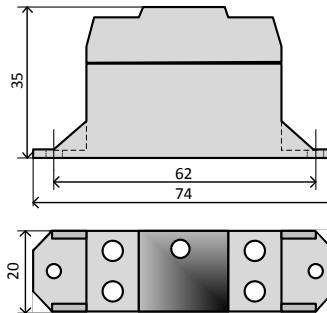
Габаритные размеры устройства для монтажа на поверхность
